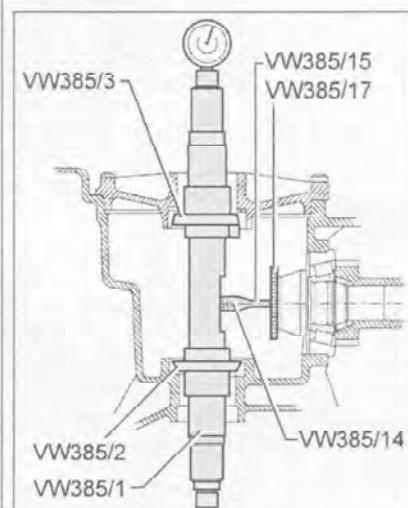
Установите приспособление MP 3-405/17 (VW 385/17) на ведущую шестерню.
